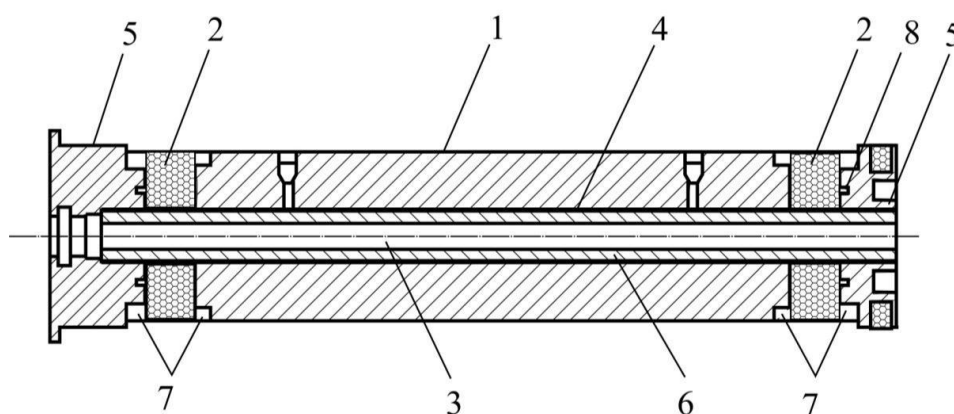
Демпфуючі пристрої для борштанги і заготовки
